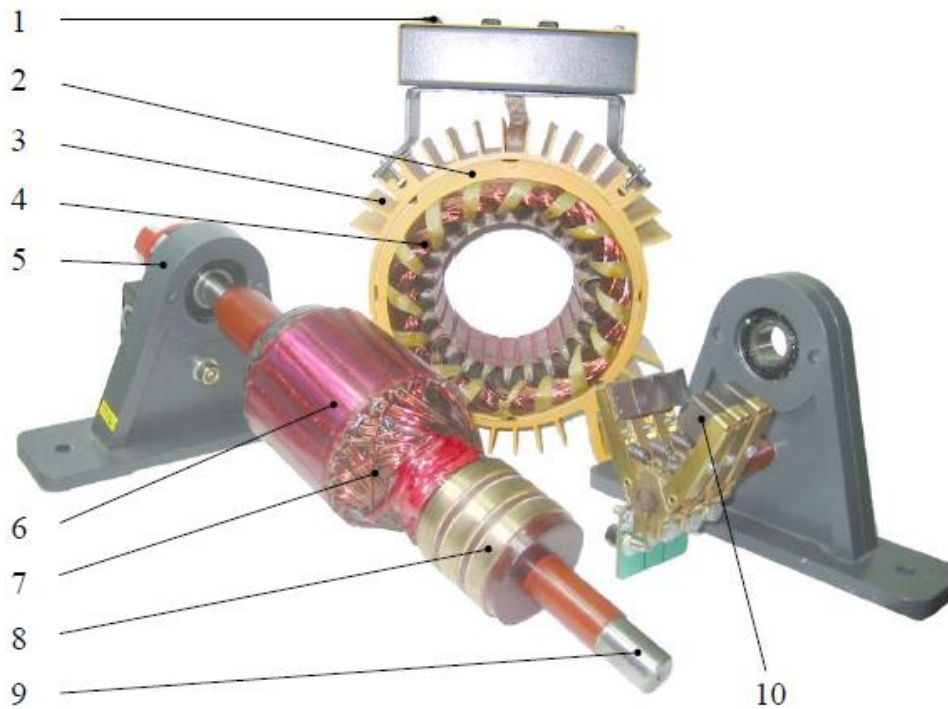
Mașină asincronă cu rotor bobinat – variantă didactică
